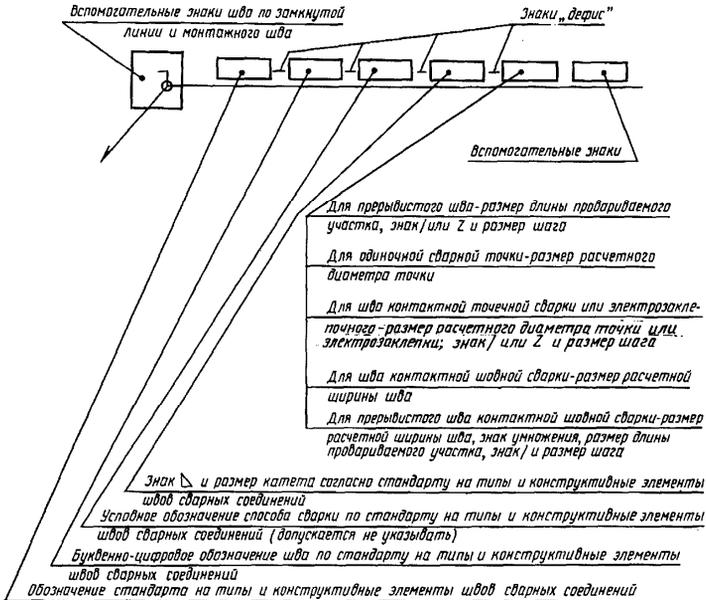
Структура условного обозначения стандартного сварного шва
